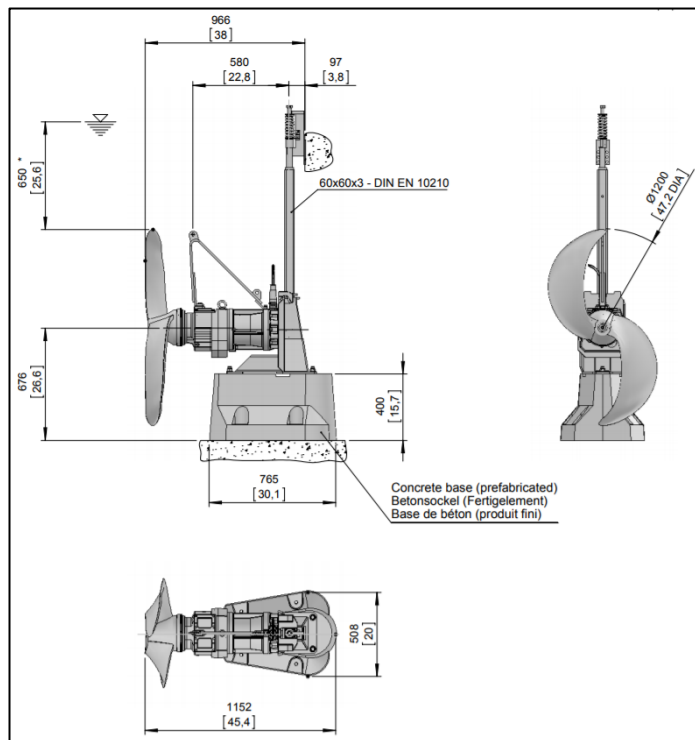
Alzado, planta y perfil de agitador de 1200 mm de diámetro
